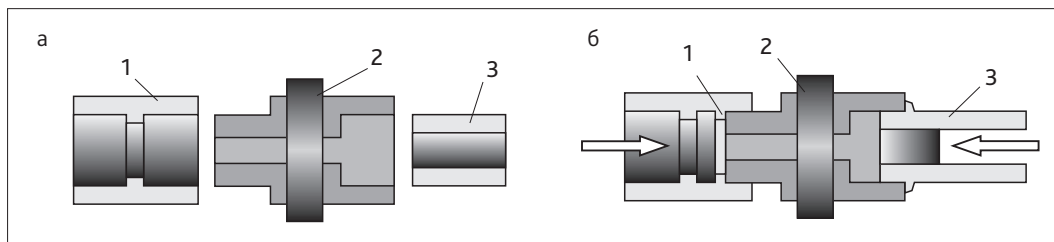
Сварка труб из PE-RT тип II НИ внахлест: а – положение элементов перед сваркой, б – введение НИ в муфту и трубы в НИ (стрелки): 1 – муфта, 2 – НИ, 3 – труба
